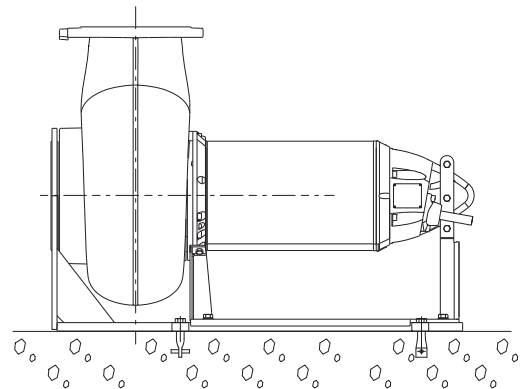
Установка на опоре для «сухого» горизонтального монтажа
